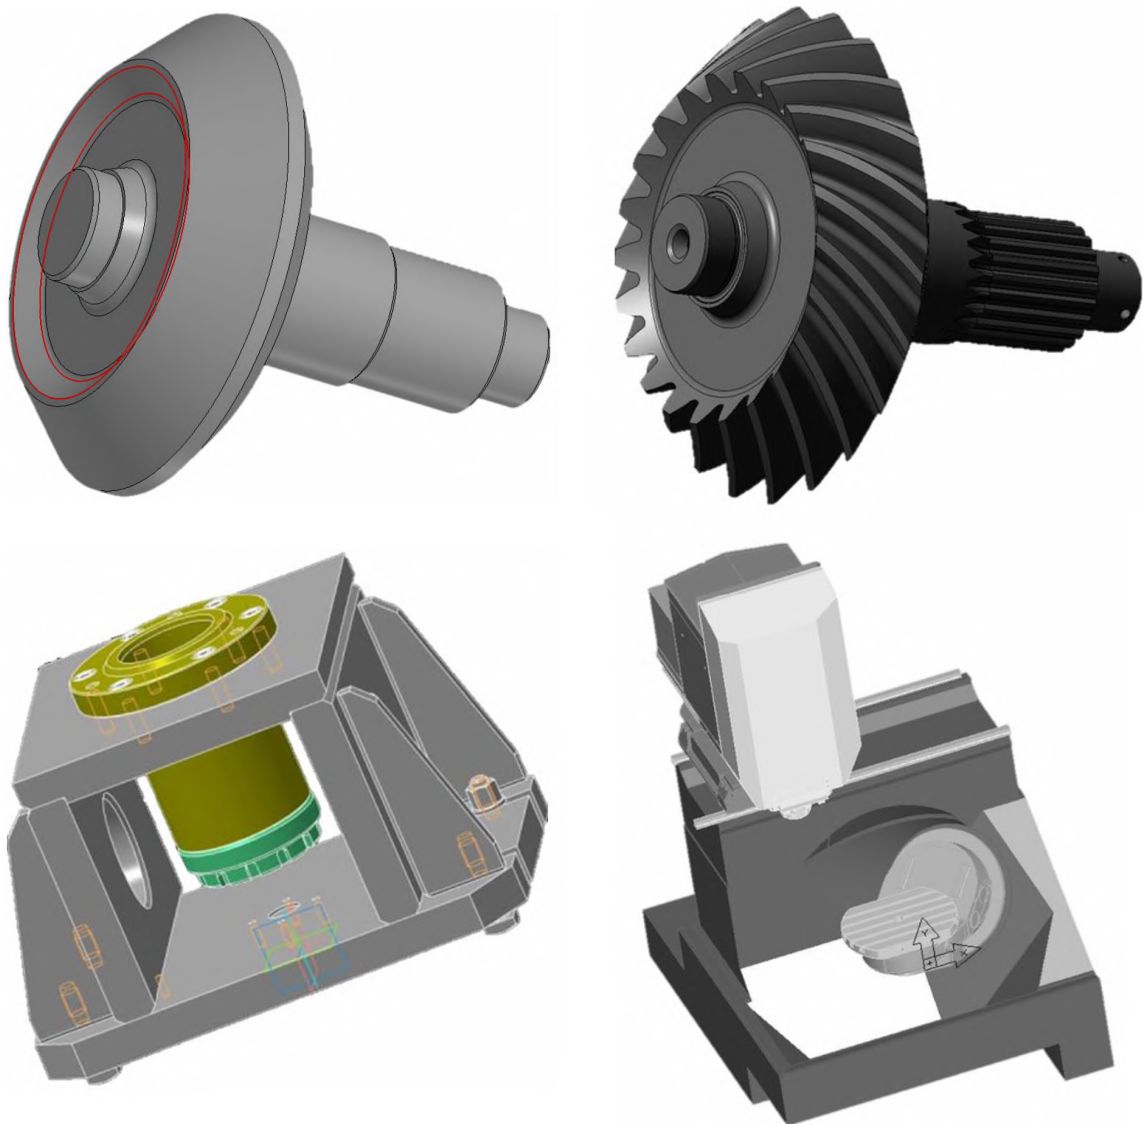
Модель заготовки, готової деталі, оснащення та верстату
